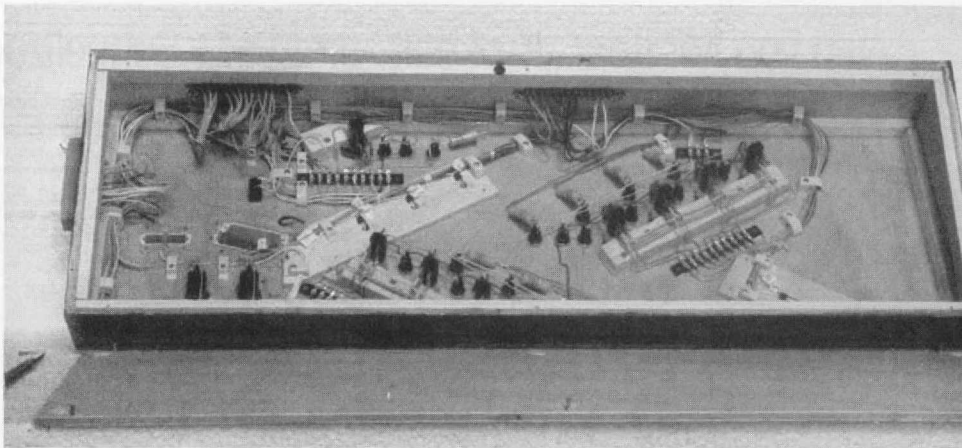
„Wie's drinnen aussieht“, kann der Erbauer ruhig zeigen, denn er hat sehr exakt gearbeitet und z. B. die Kabel gebündelt geführt und mit Schellen befestigt.
